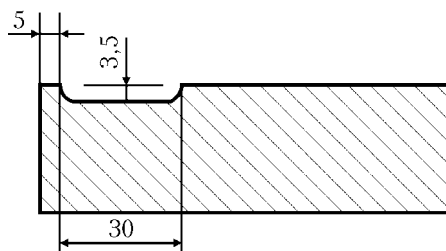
Схема типичного поперечного сечения заготовки ножа с канавкой
